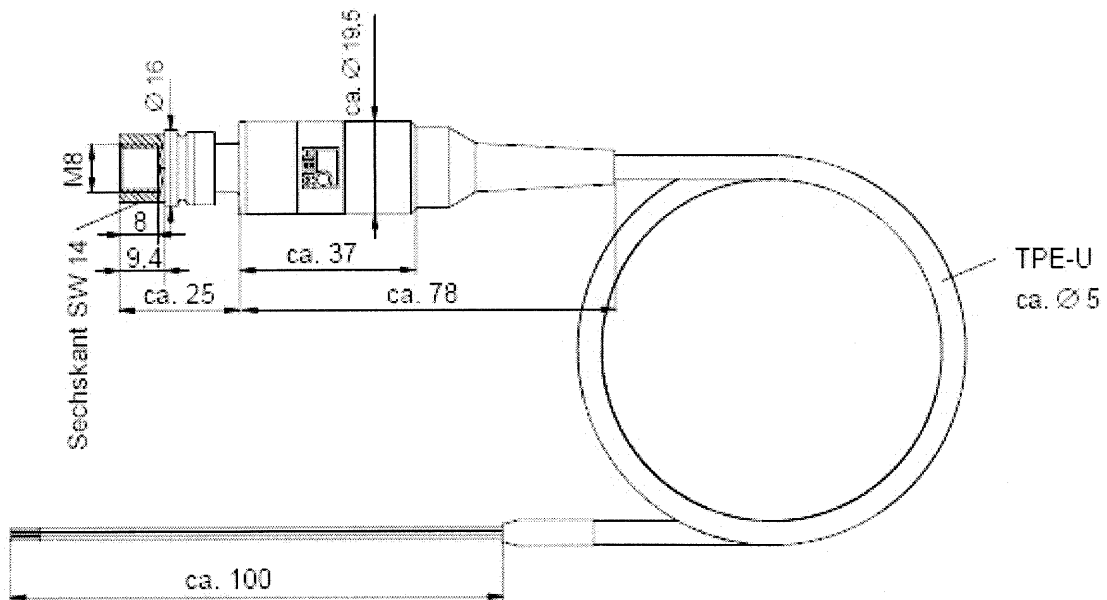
Abmessungen des Drucksensors Typ P8AP in mm
